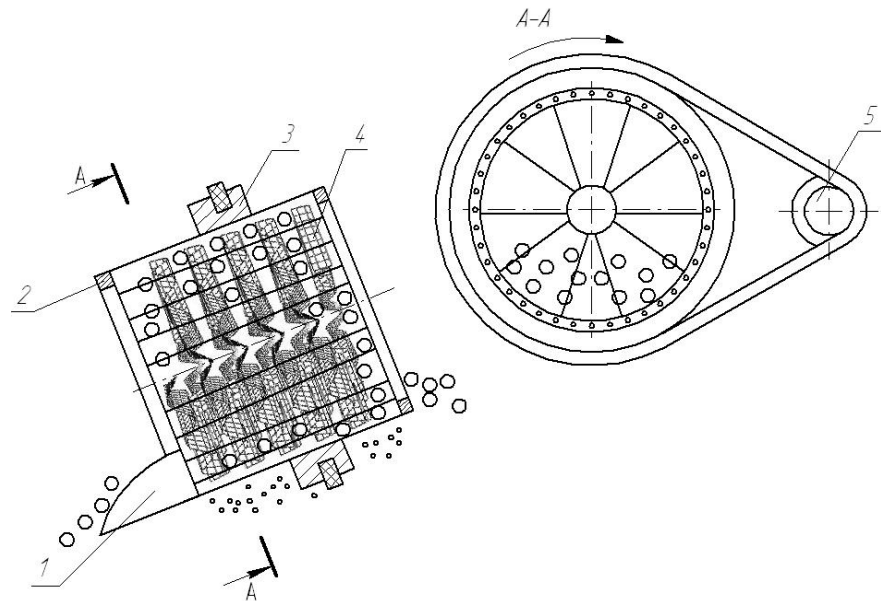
Конструкція очисника коренеплодів: 1 – завантажувач; 2 – корпус барабана; 3 – ведений шків; 4 – профільна гвинтова заготовка; 5 – привід
